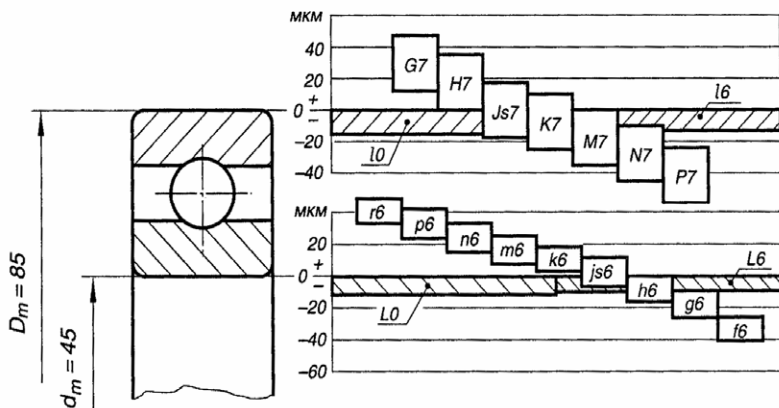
Схема полей допусков внутренних и наружных колец подшипника
